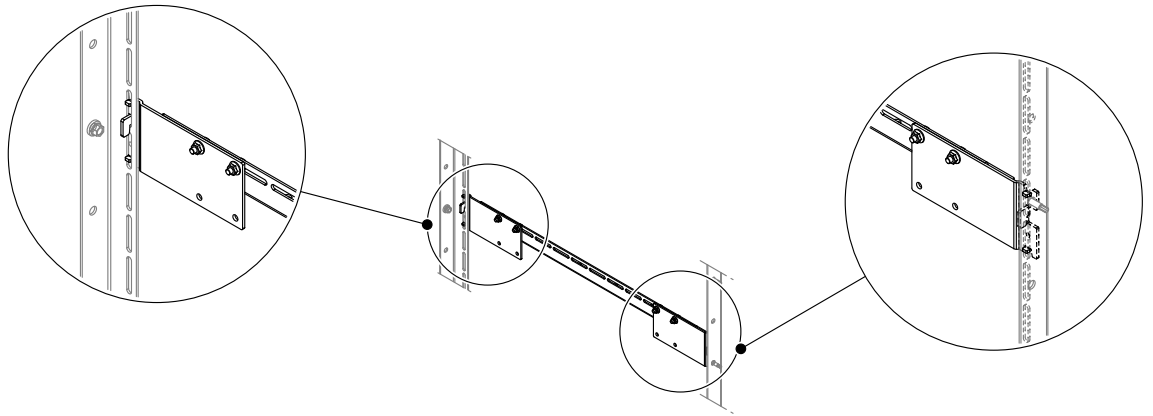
Colocación de travesaños para el montaje de refuerzos en instalaciones de hasta 2100 mm
